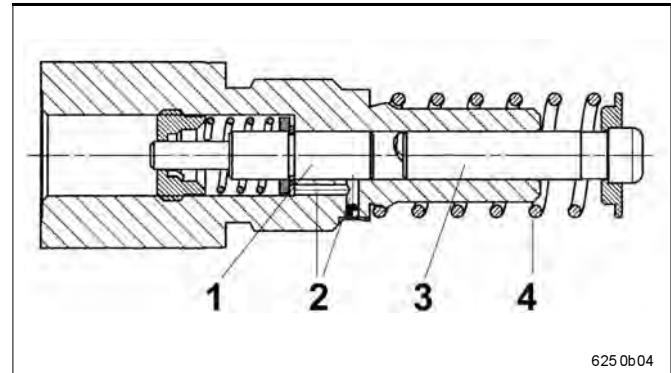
Schnittdarstellung Pumpenelement B7
